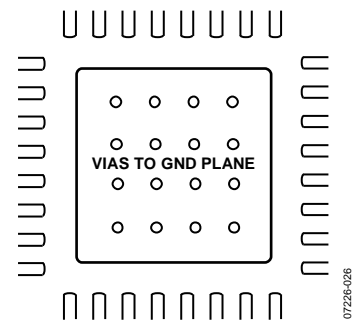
连接裸露焊盘的PCB焊盘示例
